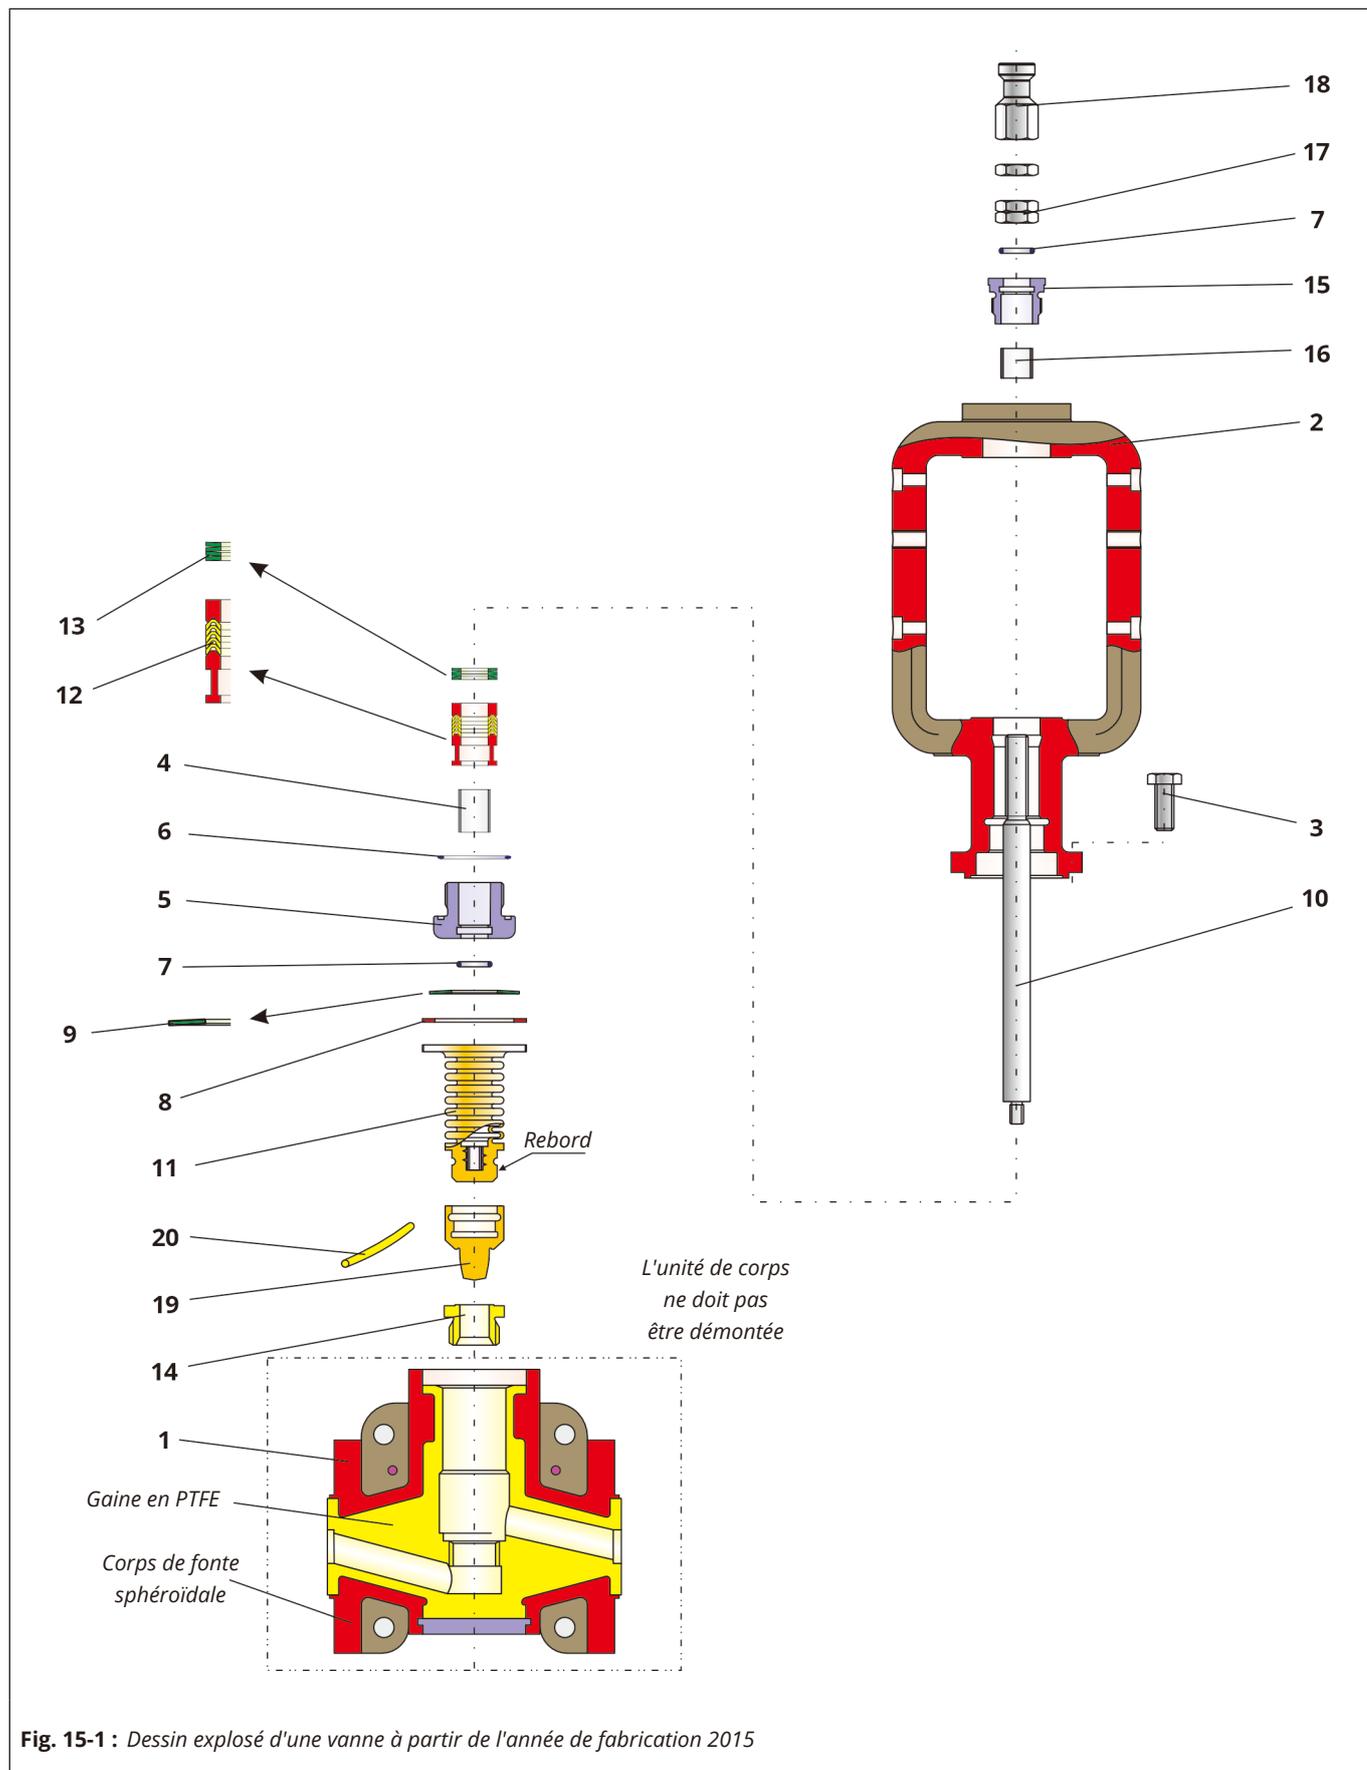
Dessin explosé d'une vanne à partir de l'année de fabrication 2015
